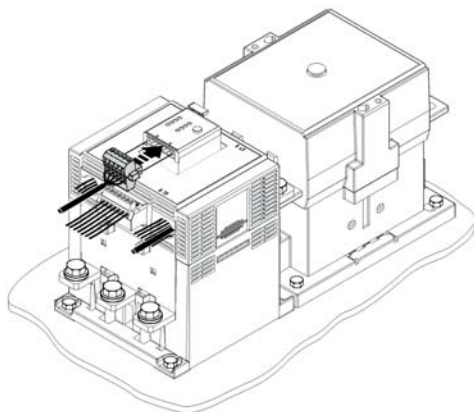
Instrucciones de ensamblaje del arrancador 100-D95...D860
